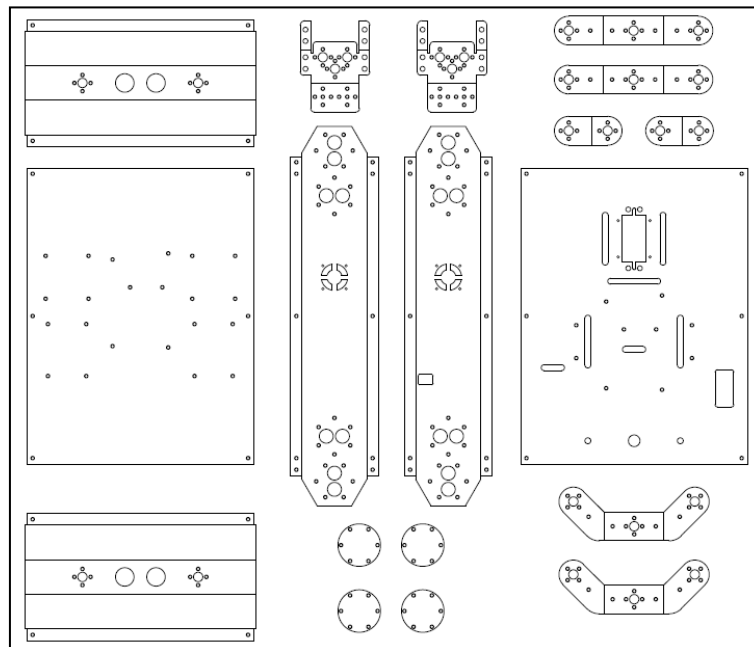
Desenho das partes mecânicas - Fonte: Autoria Própria
